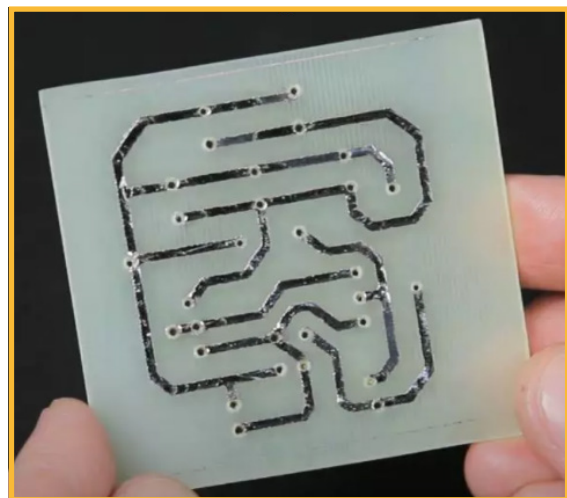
Placa PCB manufactura personal. Fuente: Hardzone.
